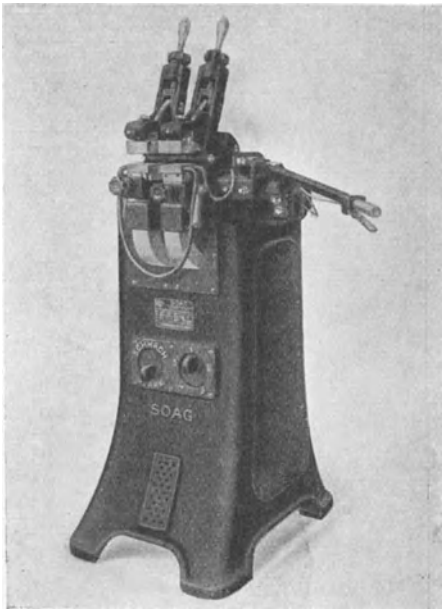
Kleine Stumpfschweißmaschine.
